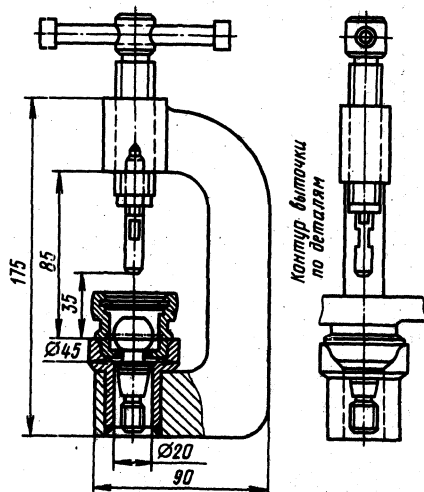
Приспособление для сборки шарниров рулевых тяг автомобиля «Москвич»
